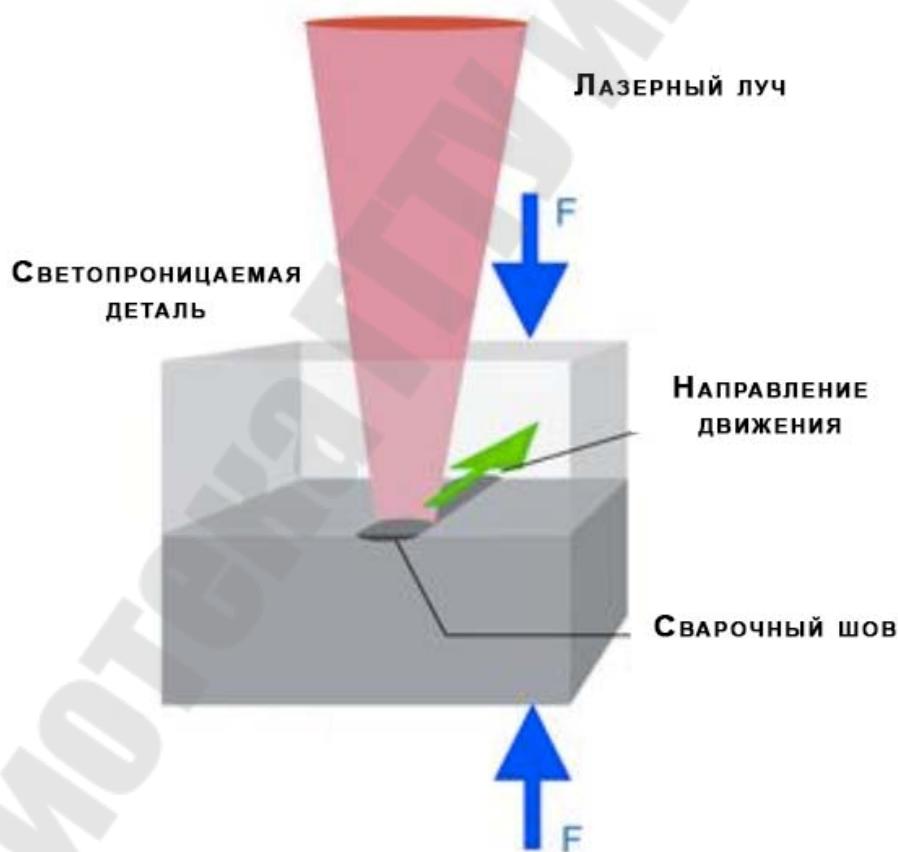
Схема проведения сварки полимеров лазерным излучением
